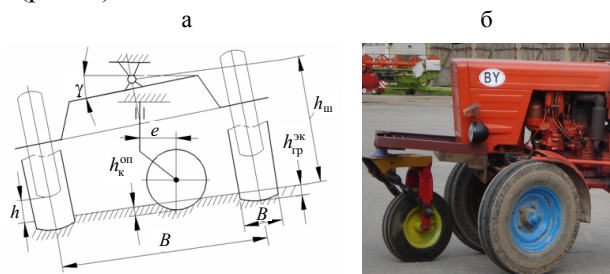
Опорно-маневровое устройство: а – схема установки; б – макетный образец
